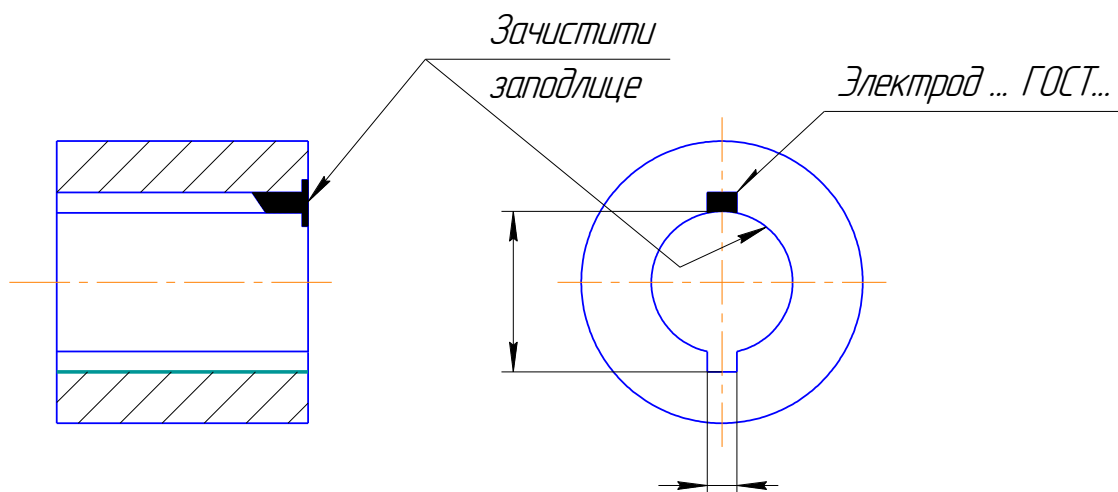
Приклад зображення використання зварювання, паяння
